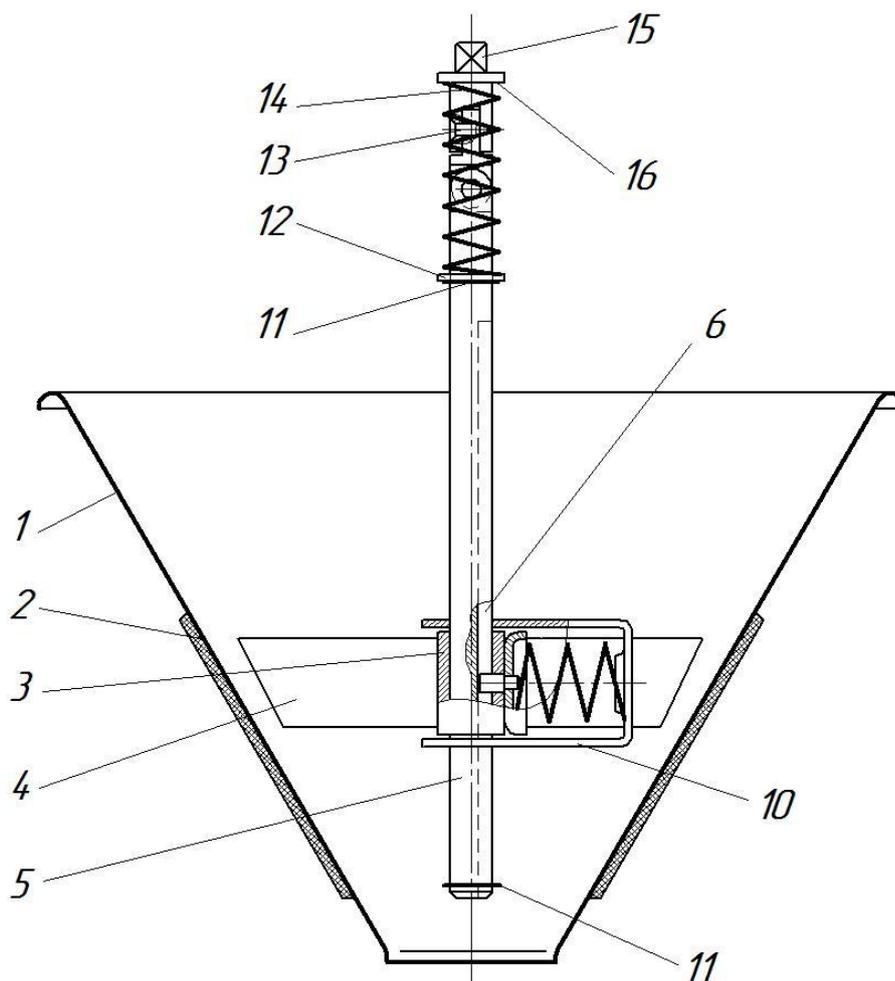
Устройство для сбора масла, общий вид.
